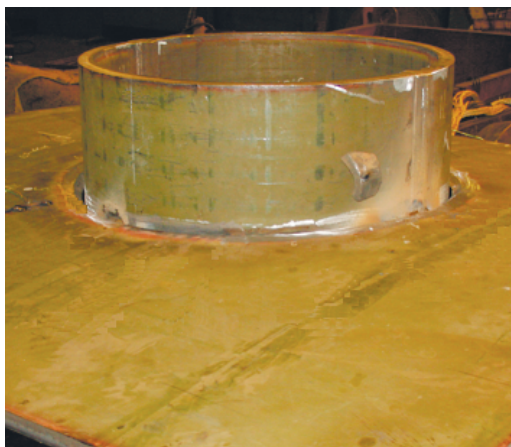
Фотография конструкции с кольцевым сварным швом.
